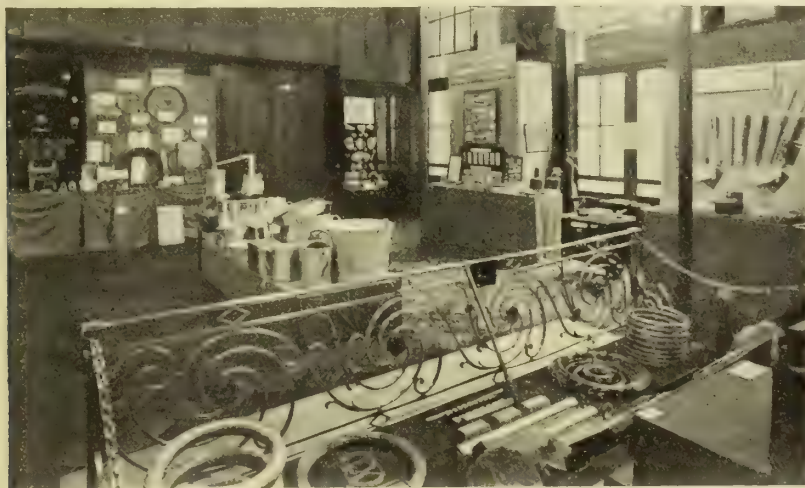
Soudure autogène. Bronzes d'aluminium et matériel de chaudronnerie en aluminium.
